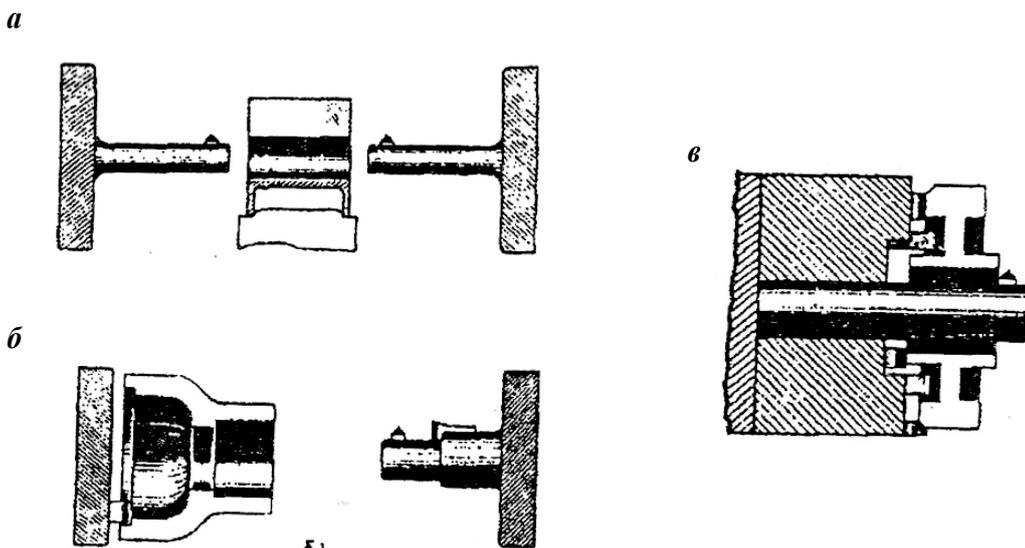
Схемы растачивания отверстий с установкой и закреплением детали на столе станка: а – на горизонтально двустороннем станке; б – на горизонтально одностороннем станке (последовательное растачивание двух отверстий); в – на горизонтальных одно- и двустороннем станках с применением многолезвовой наладки
